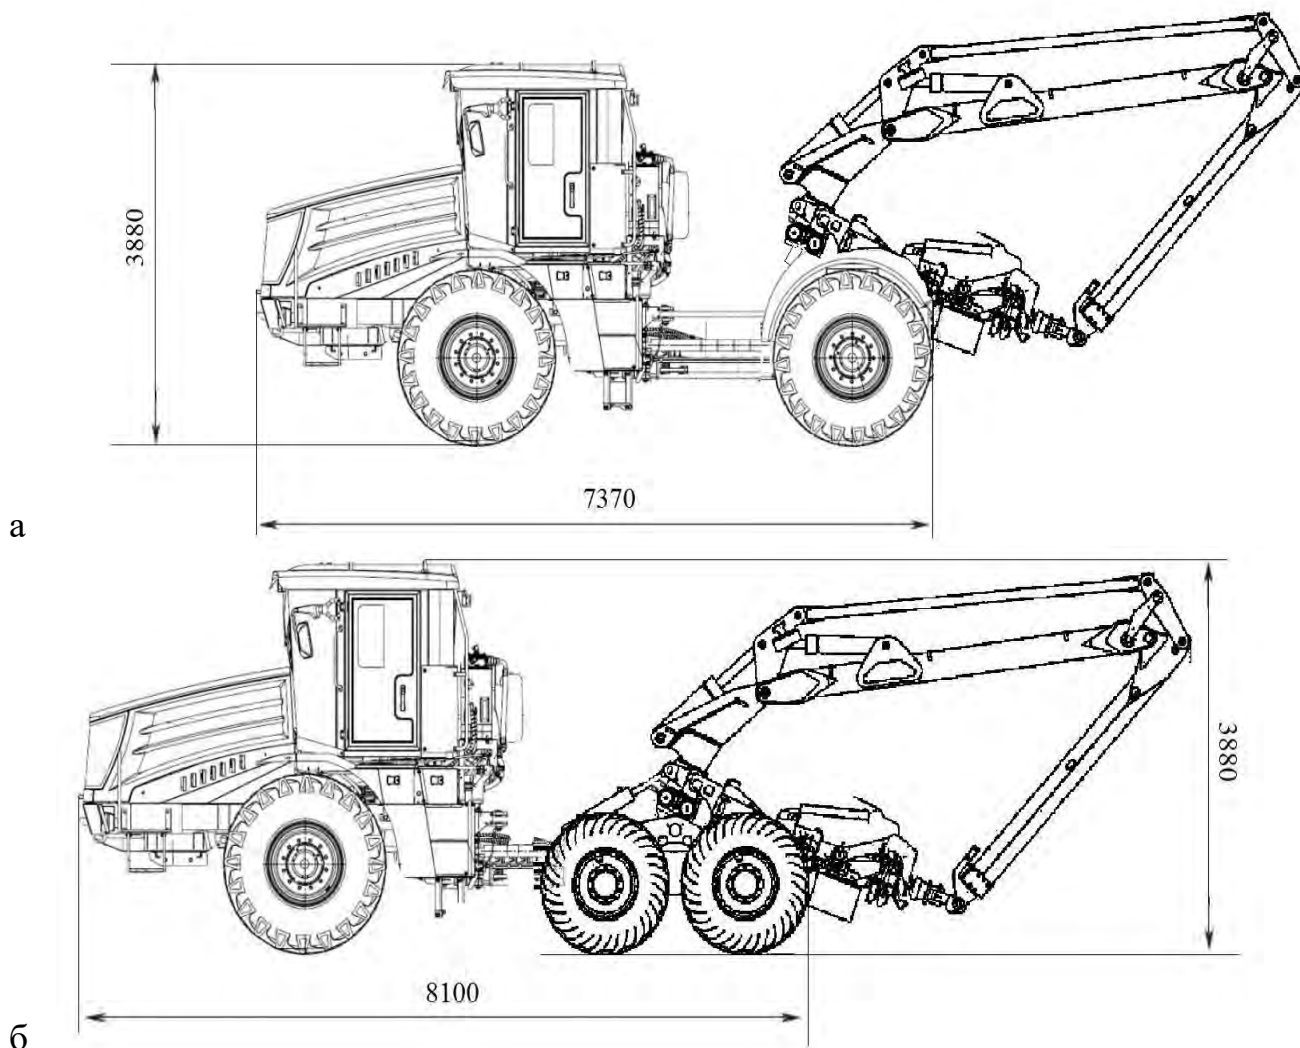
Схема колесного харвестера на базе трактора «Кировец»: а) с колесной формулой 4х4; б) с колесной формулой 6х6
